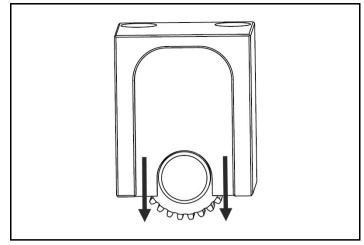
Quitar la cubierta de la caja de engranajes
